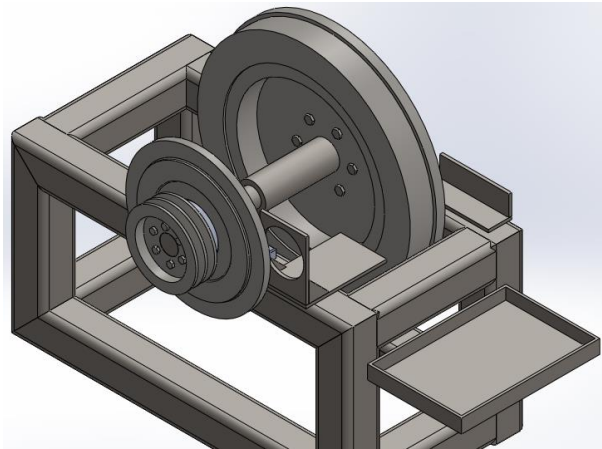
Modelo CAD del ensamble del eje con volantes instalado en la estructura portante del banco.
